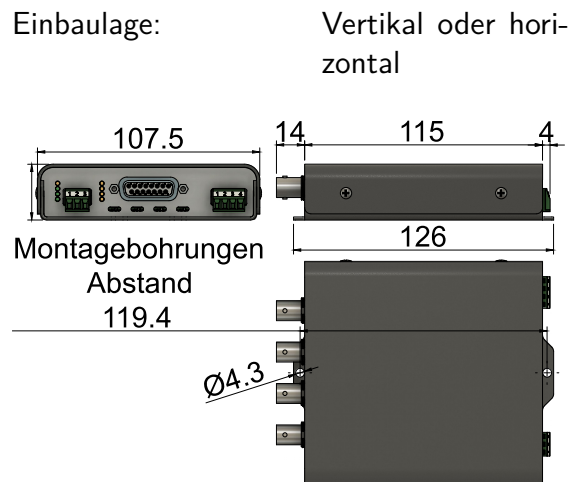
Baugruppe Mechanik: Abmessungen, Einbau
